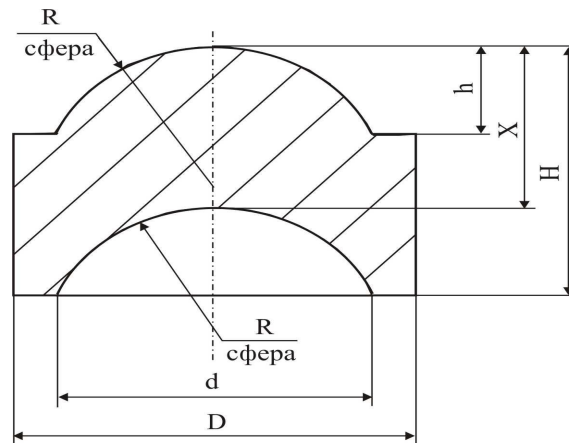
Пресовка для видавлювання алюмінієвого прутка
